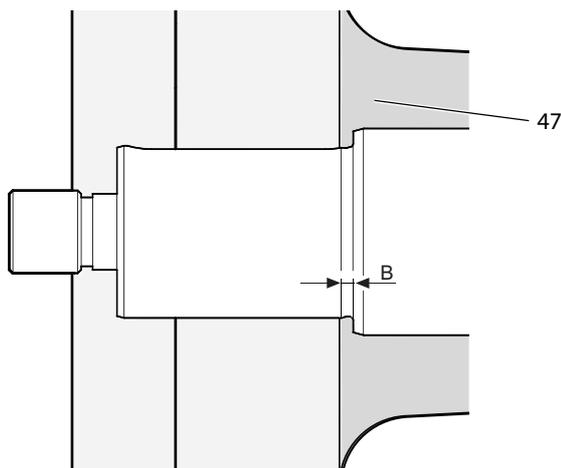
Messung Spaltmaß Wellenschulter/Pumpengehäuse
